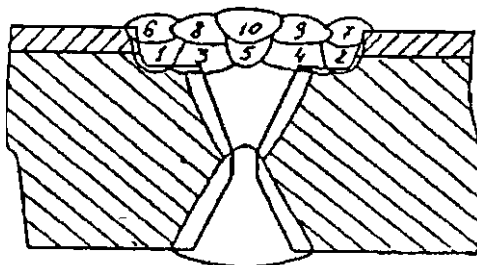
Последовательность ремонтной сварки плакирующего слоя
